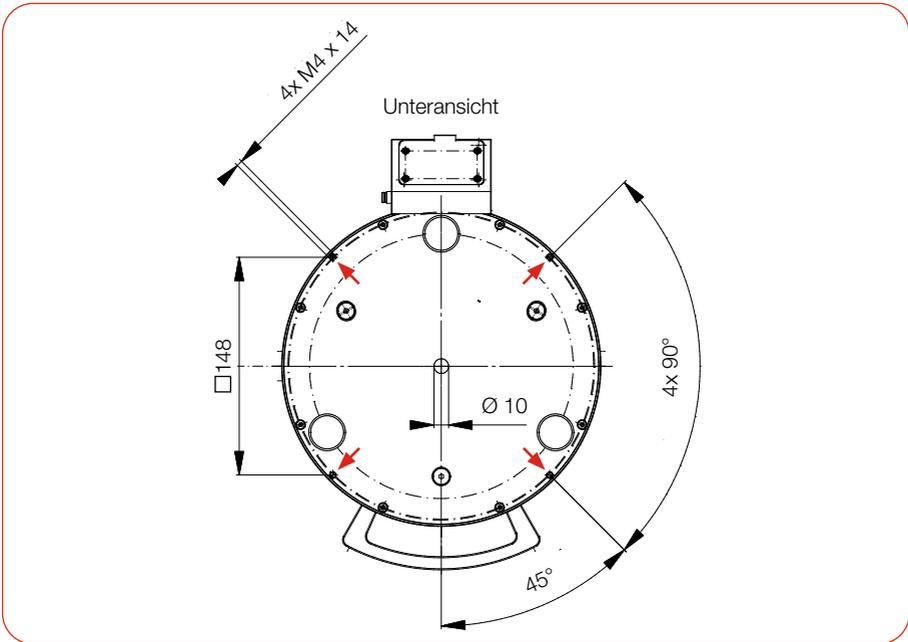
Befestigungsgewinde im Gehäuse (Maße in mm)
